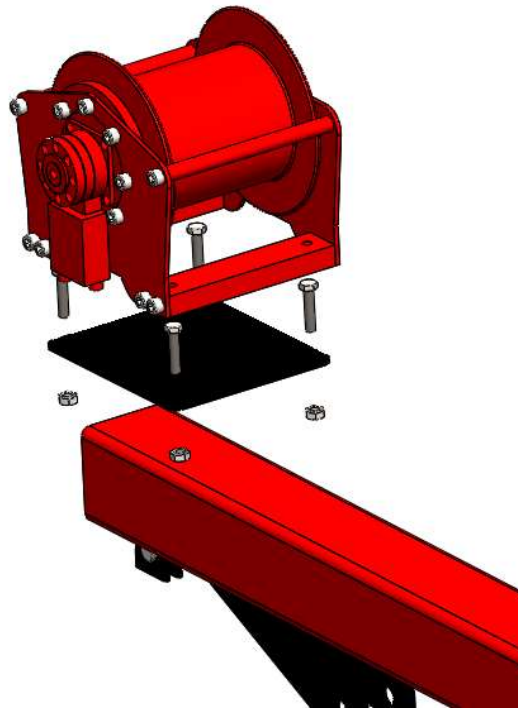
Vista explosionada del ensamblaje del cabrestante.
